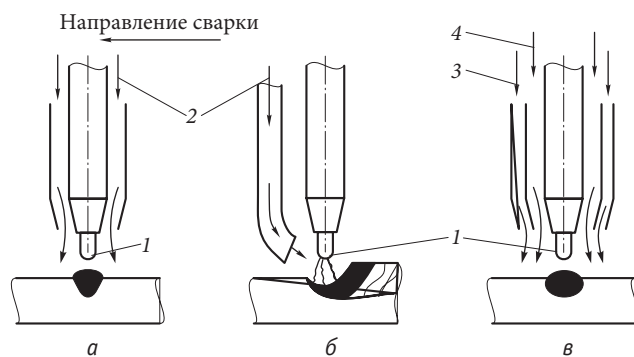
Схемы газовых потоков в зоне сварки:
